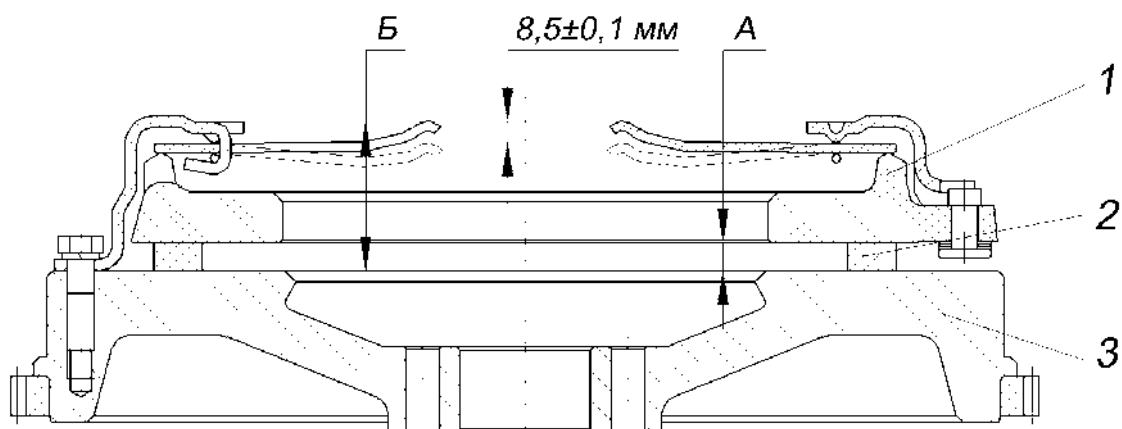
Регулировка концов лепестков и проверка нажимного диска сцепления:
